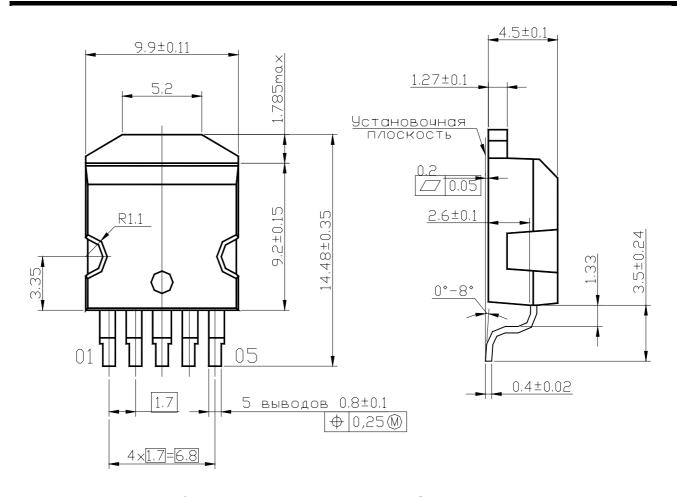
Габаритный чертеж корпуса 1501Ю.5-А
